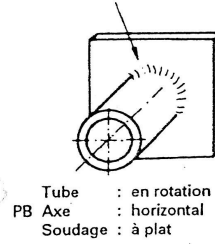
Positions de soudage pour les assemblages de tôles
